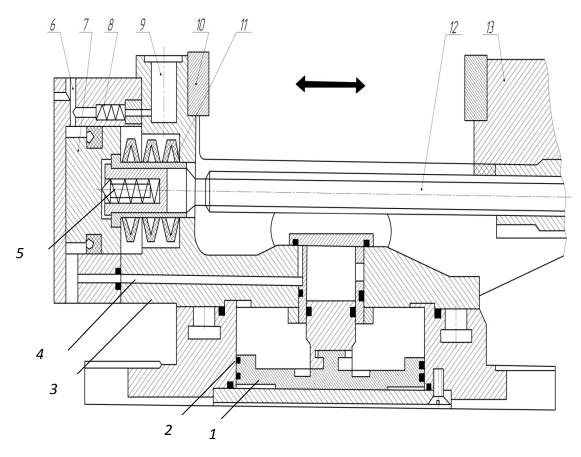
Тиски со встроенным пневмогидравлическим преобразователем давления: 1 — пневмопоршень; 2 — уплотнение; 3 — делительный стол; 4 — канал; 5 — пружина; 6 — узел выпуска воздуха; 7 — гидропоршень; 8 — обратный клапан; 9 — емкость; 10 — неподвижная губка; 11 — тарельчатая пружина; 12 — винт; 13 — подвижная губка
